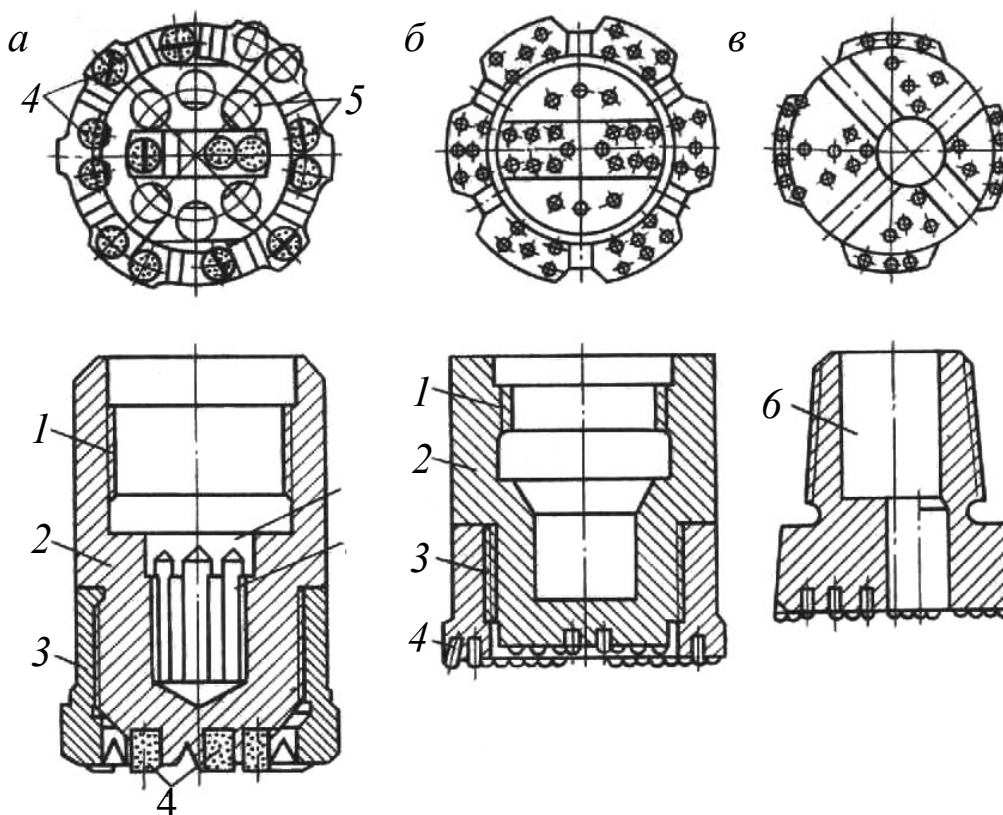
Конструкции долот для пневмоударников: 1 – соединительная резьба; 2 – корпус долота; 3 – кольцо; 4 – вставки; 5, 6 – циркуляционные каналы
